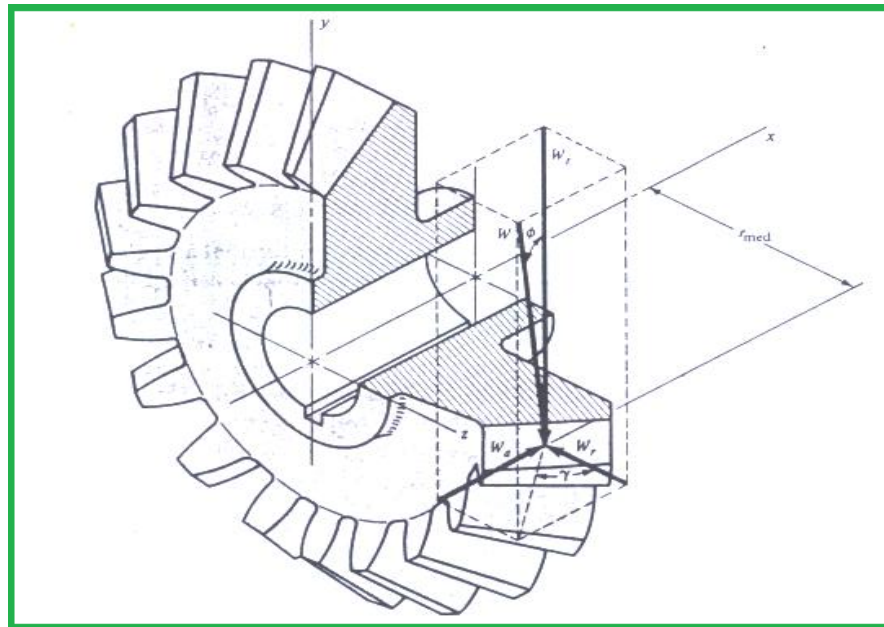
Fuerzas que actúan en los dientes de un engrane cónico
